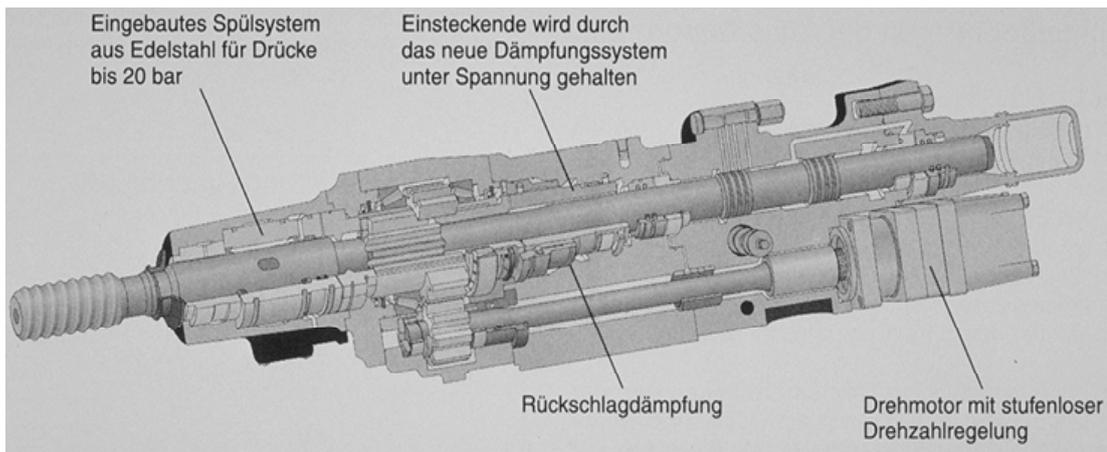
Hydraulikhammer bzw. Hydraulikdrehschlagbohrmaschine
